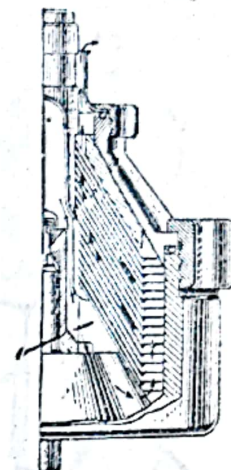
Secțiune printr'un tambur clarificator cu discuri.
